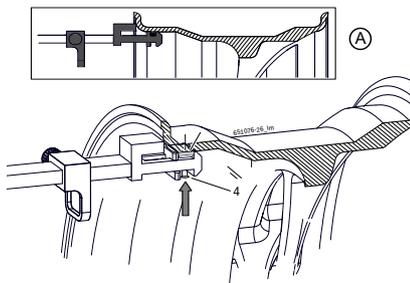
Укладка адгезивного груза в место для укладки для установки на борт обода
